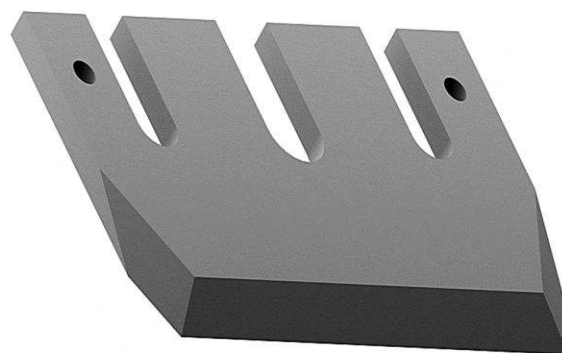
Режущий инструмент малоножевой торцово-конической фрезы
